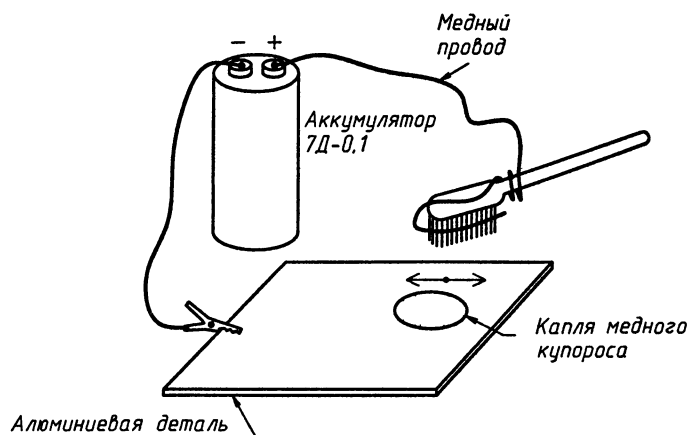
Приспособление для омеднения алюминиевой поверхности
